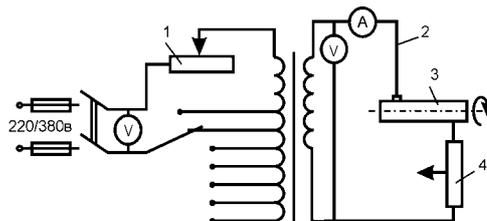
Принципиальная схема устройства для электромеханической обработки: 1 – реостат; 2 – вторичная обмотка; 3 – деталь; 4 – инструмент
